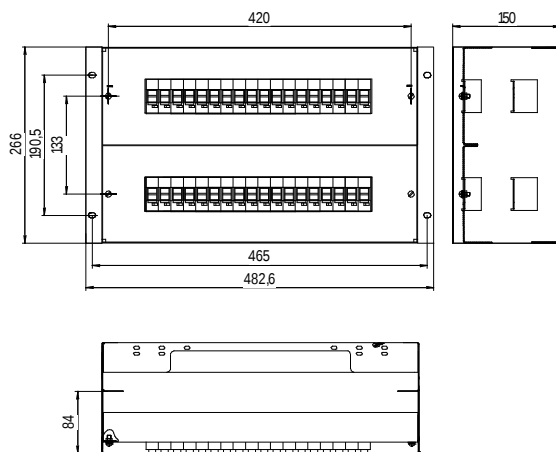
Габаритный чертеж ЩРЗ-8
